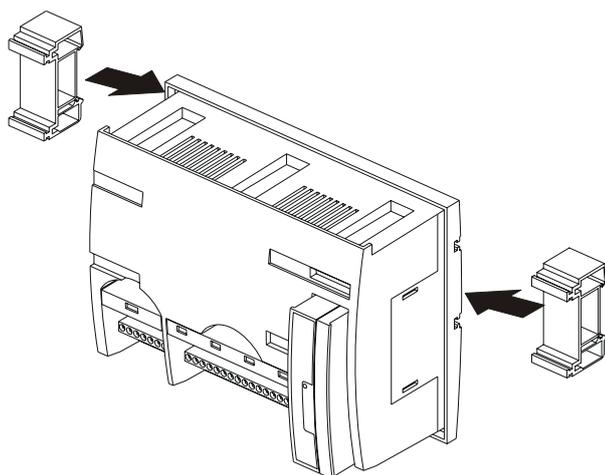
Установка контроллера без MMI внутри шкафа (а).
